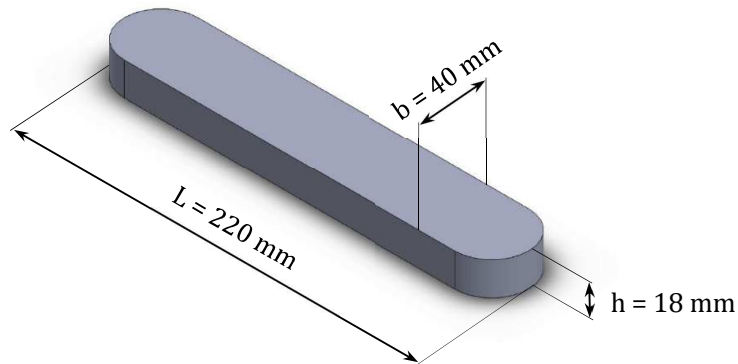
Dimensiones de la chaveta del piñón.
